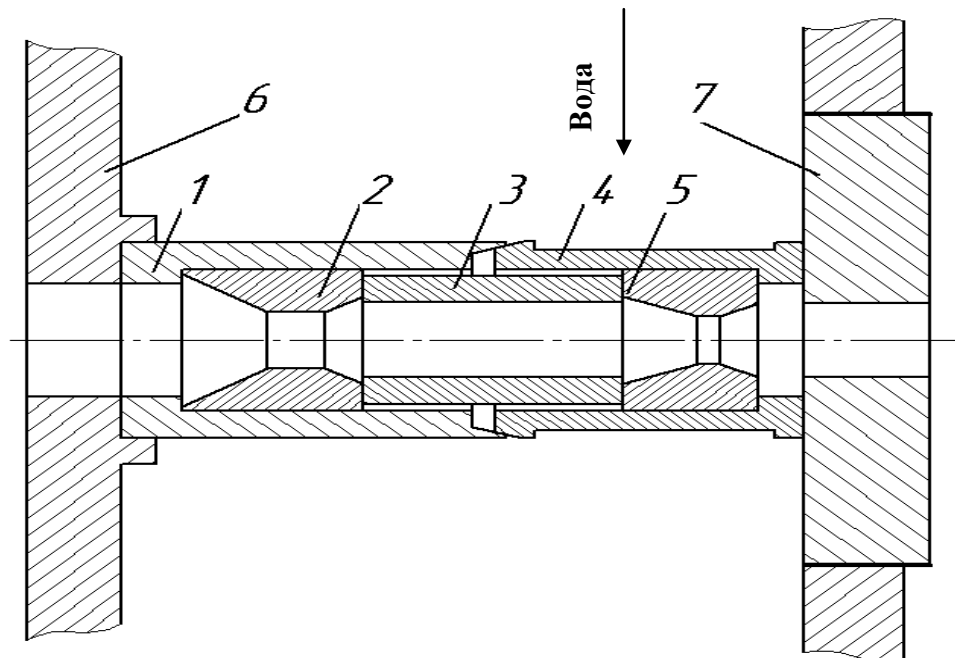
Складена водоохолоджувальна волока: 1 - корпус; 2 - напорна волока; 3 - напорна втулка; 4 - корпус робочої волоки; 5 - робоча волока; 6 - корпус мильниці; 7 - затискна гайка
